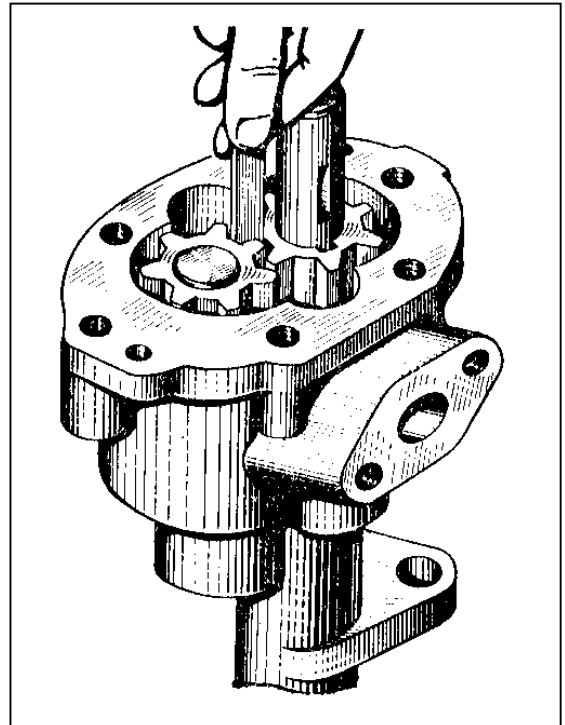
Контроль бокового зазора между зубьями зубчатых колес.
